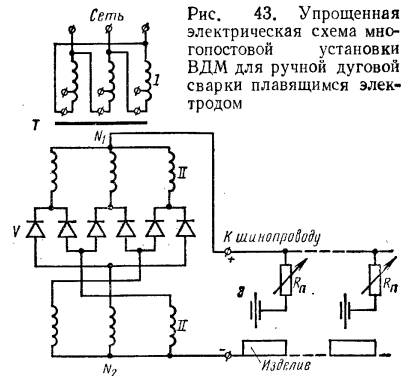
Упрощенная электрическая схема многопостовой установки ВДМ для ручной дуговой сварки плавящимся электродом
